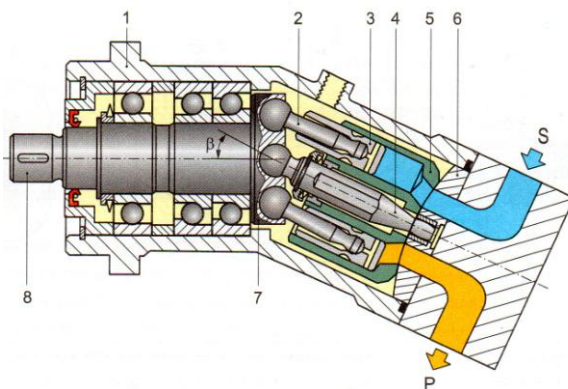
, б. Конструктивная схема аксиально-поршневого насоса с наклонным блоком: 1 – корпус; 2 – толкатель; 3 – поршень; 4 – оправка (для центрирования блока цилиндров относительно распределительного диска; 5 – блок цилиндров; 6 – распределительный диск; 7 – диск; 8 – приводной вал; S, P – линии всасывания и нагнетания.
